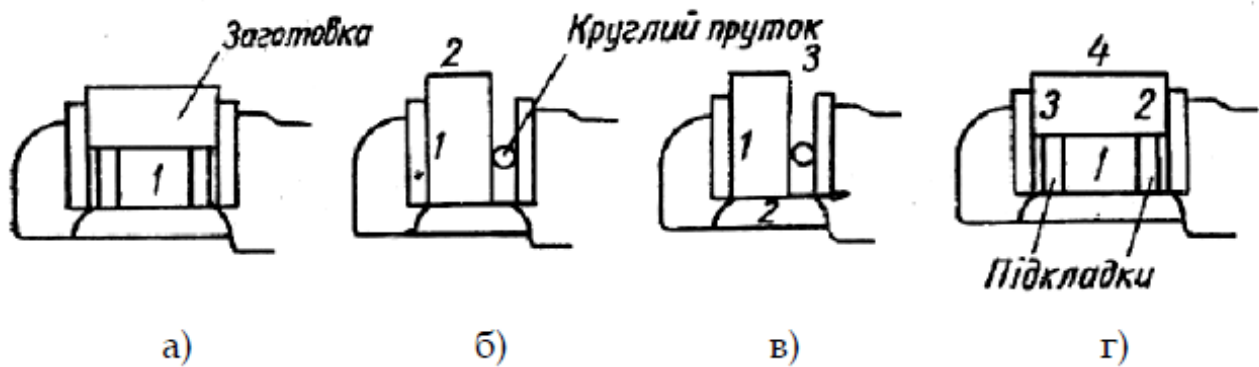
Закріплення заготовок 1, 2, 3, 4 - поверхні Після поверхні 2 обробляють поверхню 3 (рис. 2.71, в) і, нарешті, поверхню 4 (рис. 2.71, г).
